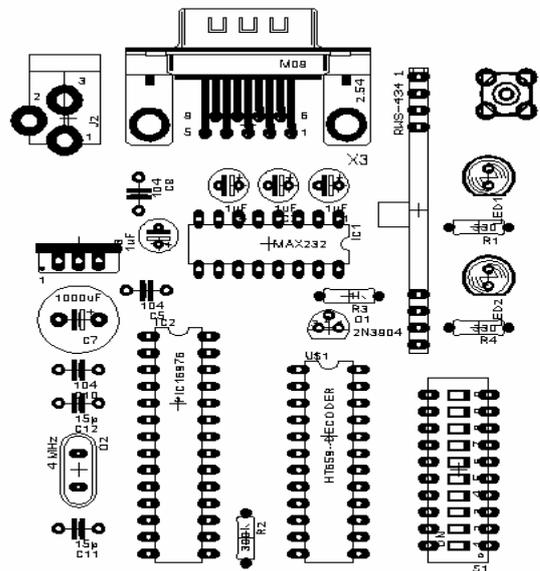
Componentes de la placa de circuito impreso del receptor
